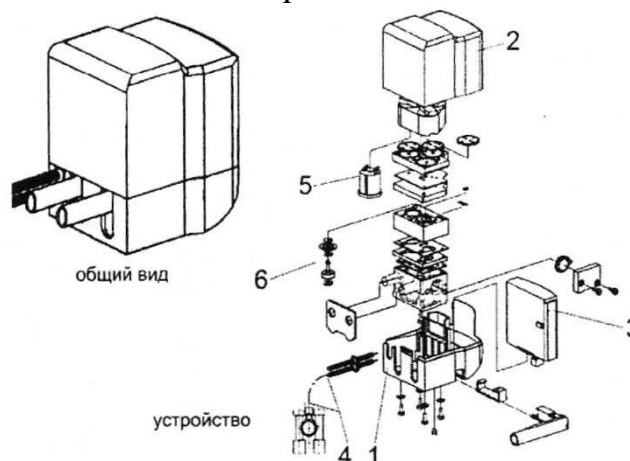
Пульсатор с электромагнитным приводом:
